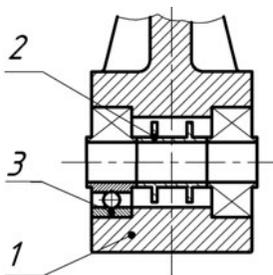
Схема установки с двухсторонней расточкой гнезд под подшипники
